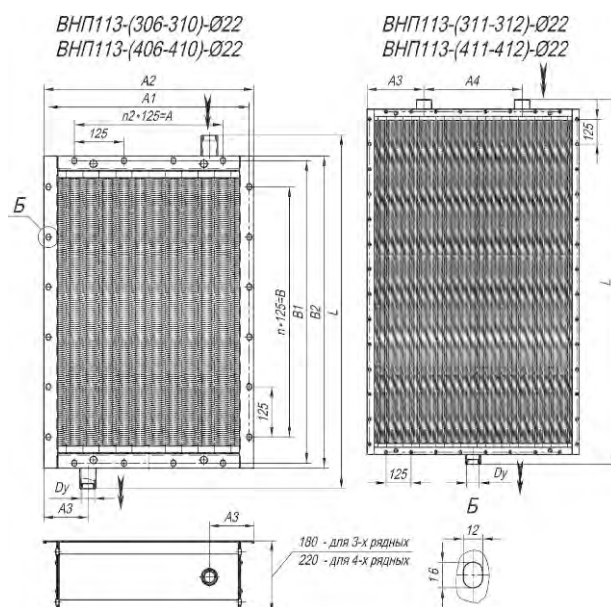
Габаритные и присоединительные размеры воздухонагревателей типа ВНП.
